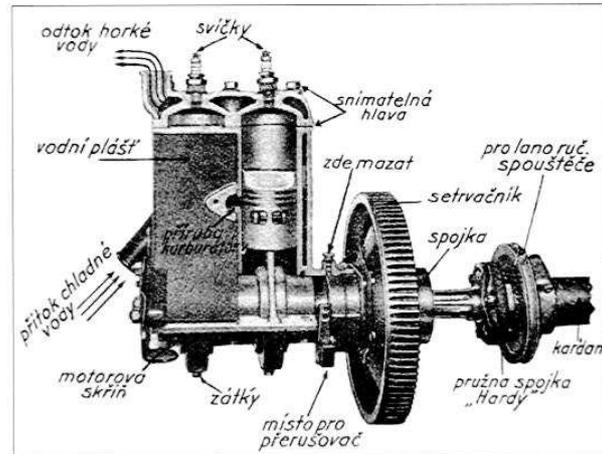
Aero 662 2-Zylinder / 2-Takt-Motor
